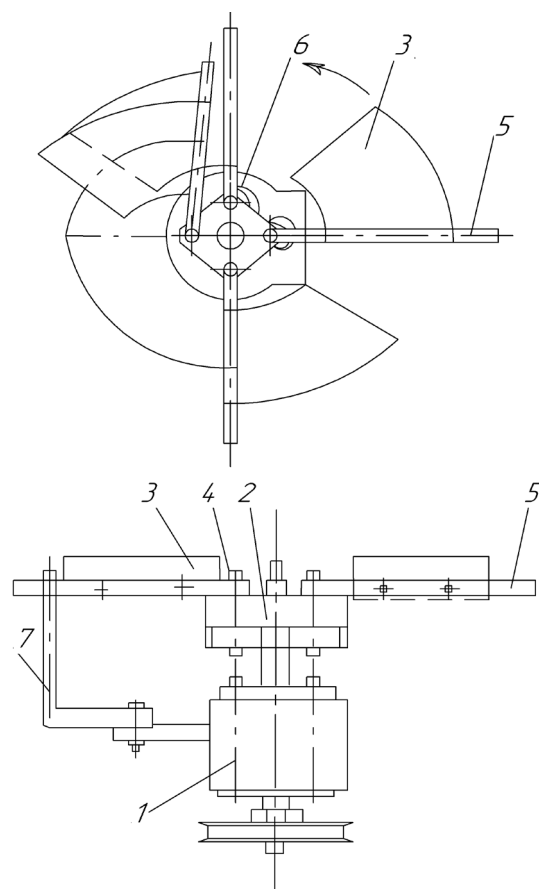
Схема відцентрового робочого органу з активними лопатками: 1 – корпус; 2- ступиця; 3 – лопатка; 4- вісь лопатки; 5 – палець; 6 – пружина; 7 – відбивач
